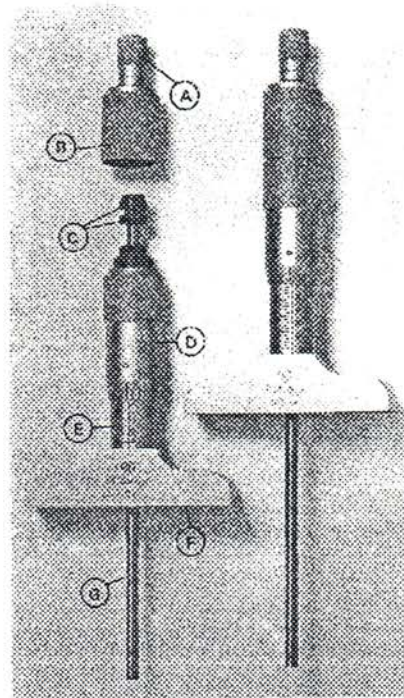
Partes del tornillo micrométrico para profundidades.
